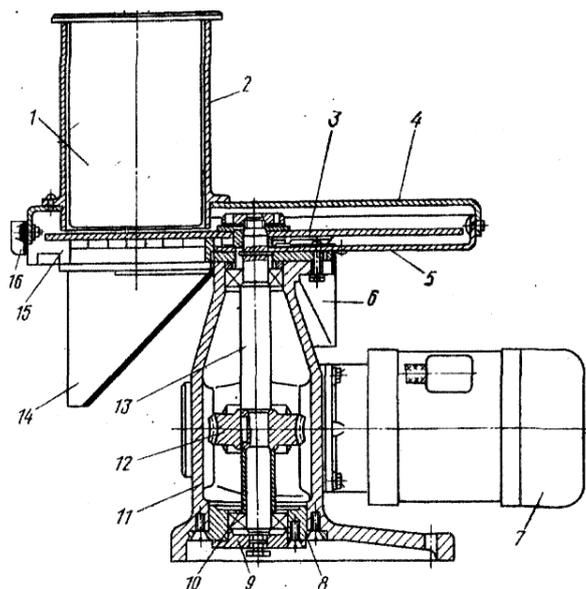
Машина для нарезки вареных овощей МРОВ-160:
